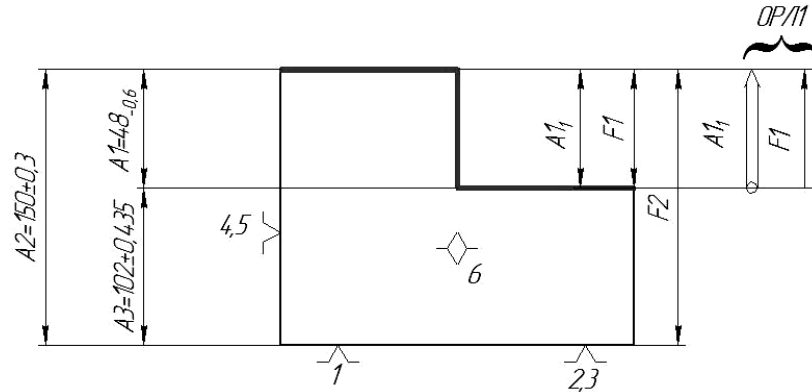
Операційний ескіз оброблення (варіант 1), фрезерування площин
